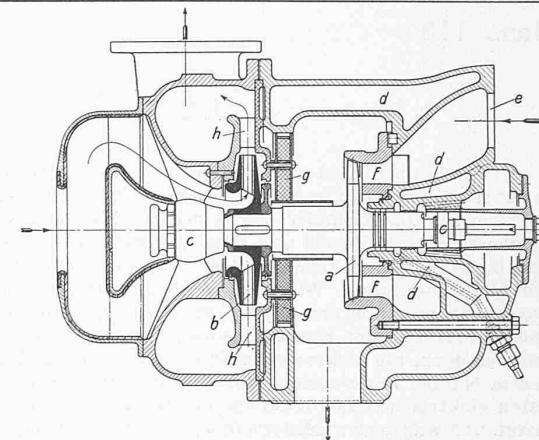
Schnitt 1:5 eines Aufladegebläses für Fahrzeugmotoren: a Turbinenrad, b Gebläserad, c Lager des Rotors, d Kühlwasserräume, e Abgaseintritt, f Düsenring, g Wärmeschutzschild, h Diffusor
